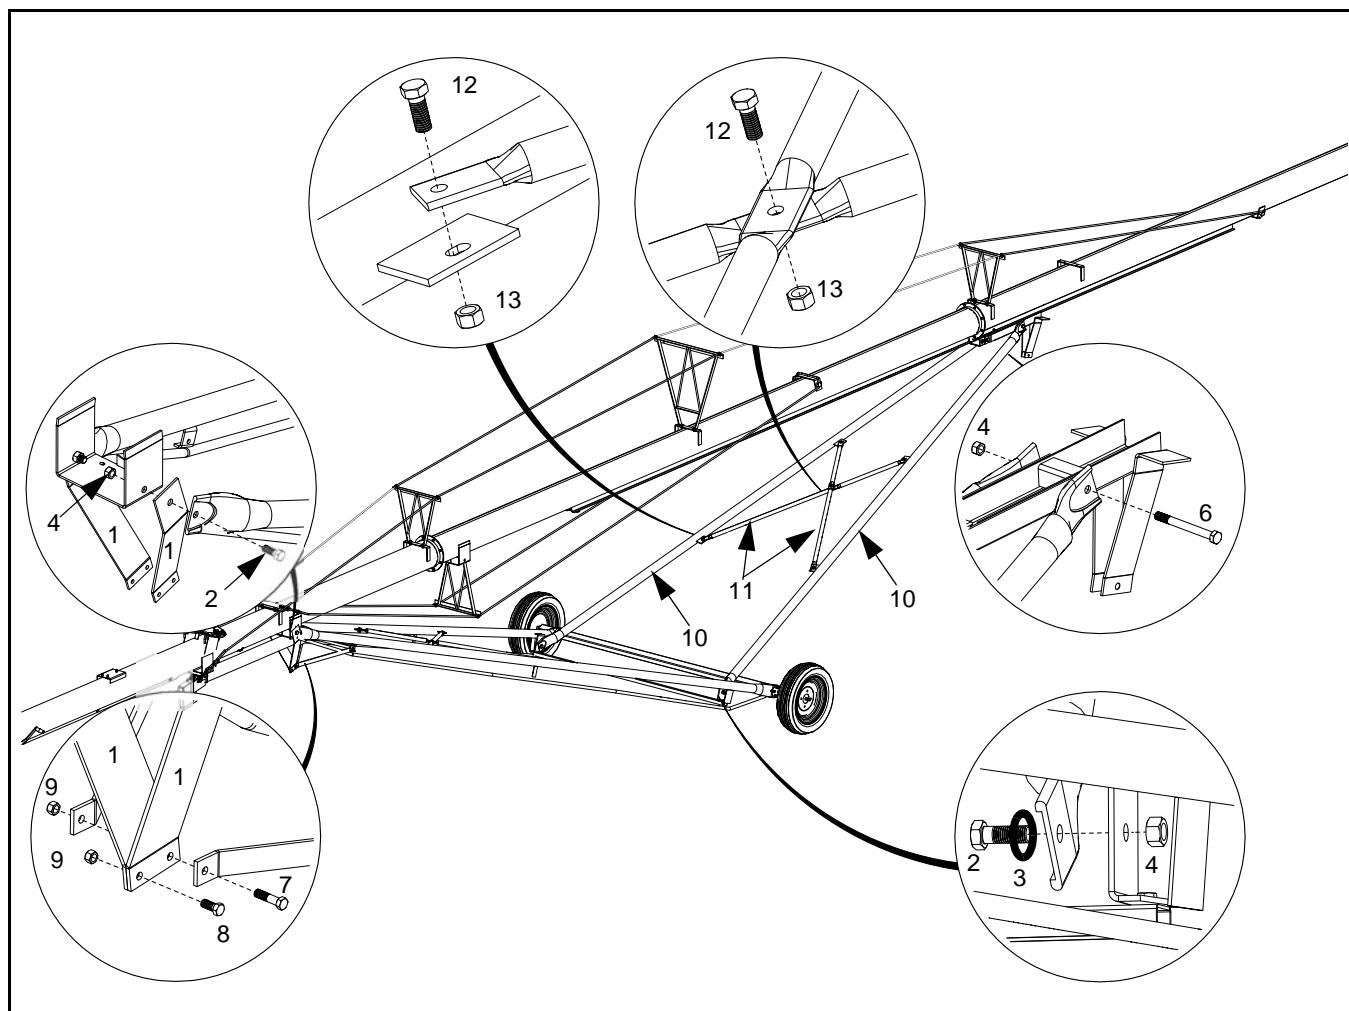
Raccord du tube de tarière au châssis (MKX100-53/63/73)
